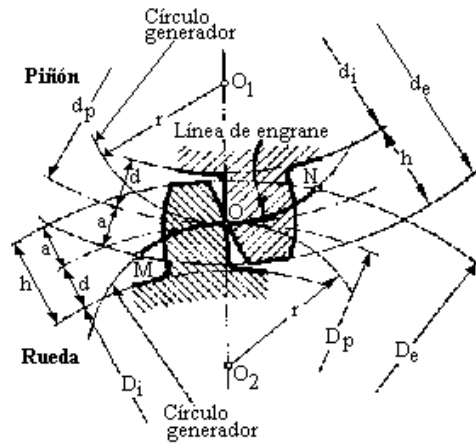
Nomenclatura de engranaje cilíndrico de diente recto.
